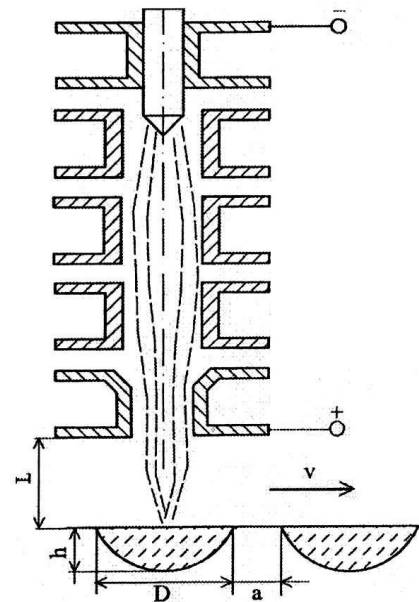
Схема плазмотрона для поверхневої обробки
